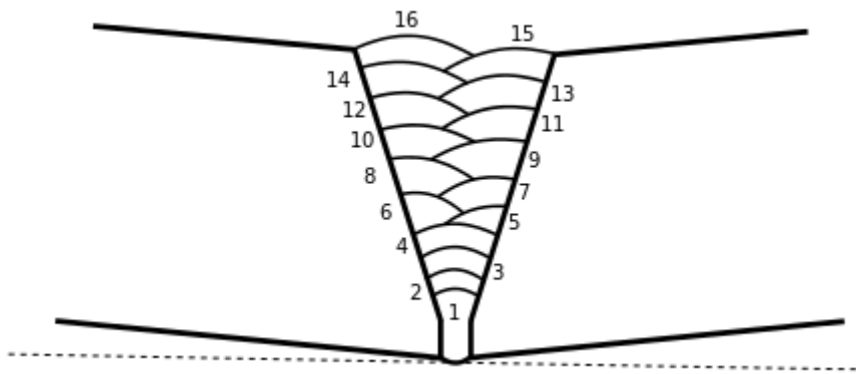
Corpo de prova 1 sem restrição – Diagrama dos passe de soldagem GTAW
